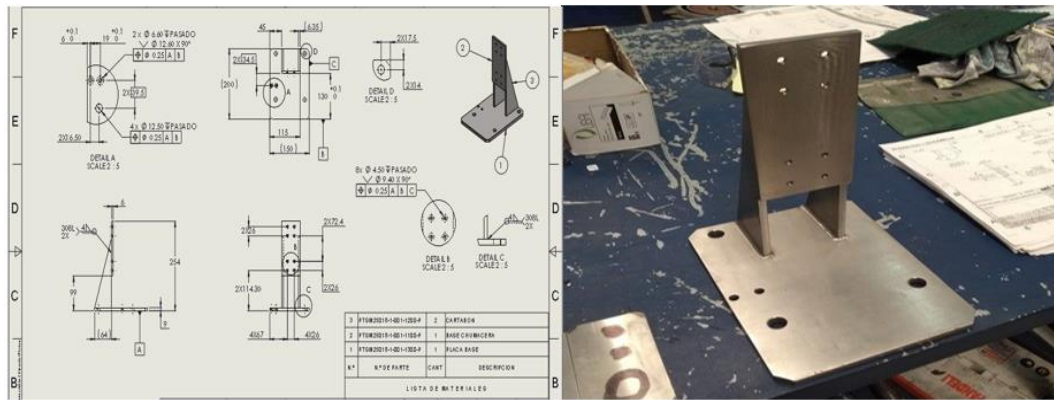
Sub-ensamble de soldadura. Base de la montura.
